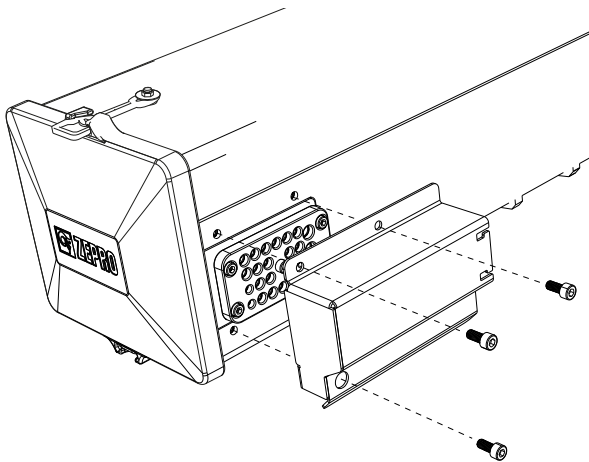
Die Schutzabdeckung der Kabeldurchführung ist mit drei Schrauben befestigt.
